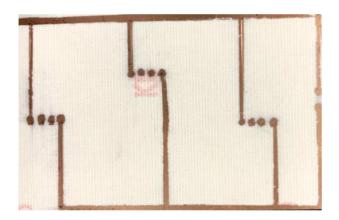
Circuito impreso desde la vista de (PCB) Fritzing en la placa de cobre
